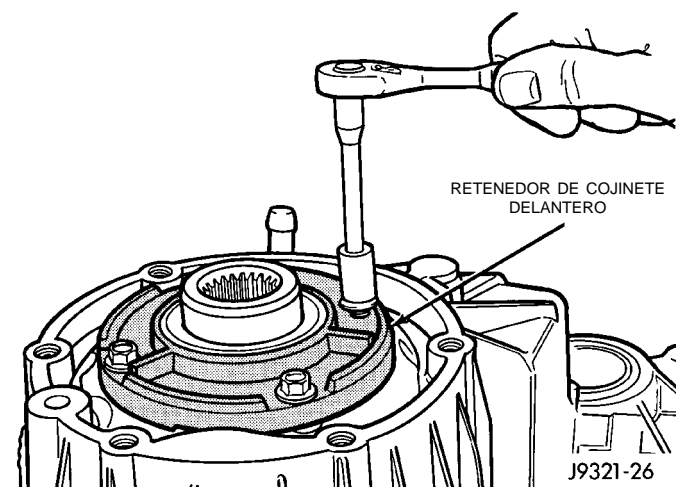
Desmontaje del perno del retenedor de cojinete delantero
